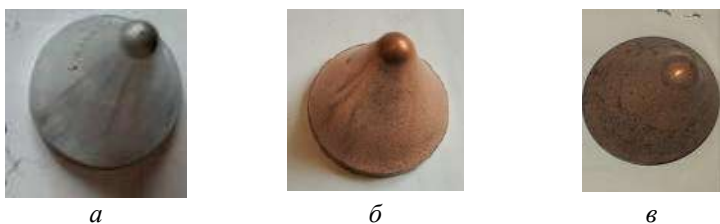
Внешний вид изготовленных кумулятивных облицовок:
